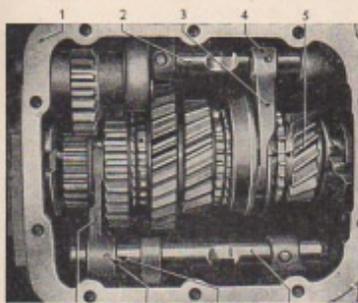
Anordnung der Schaltgabel im Getriebegehäuse
